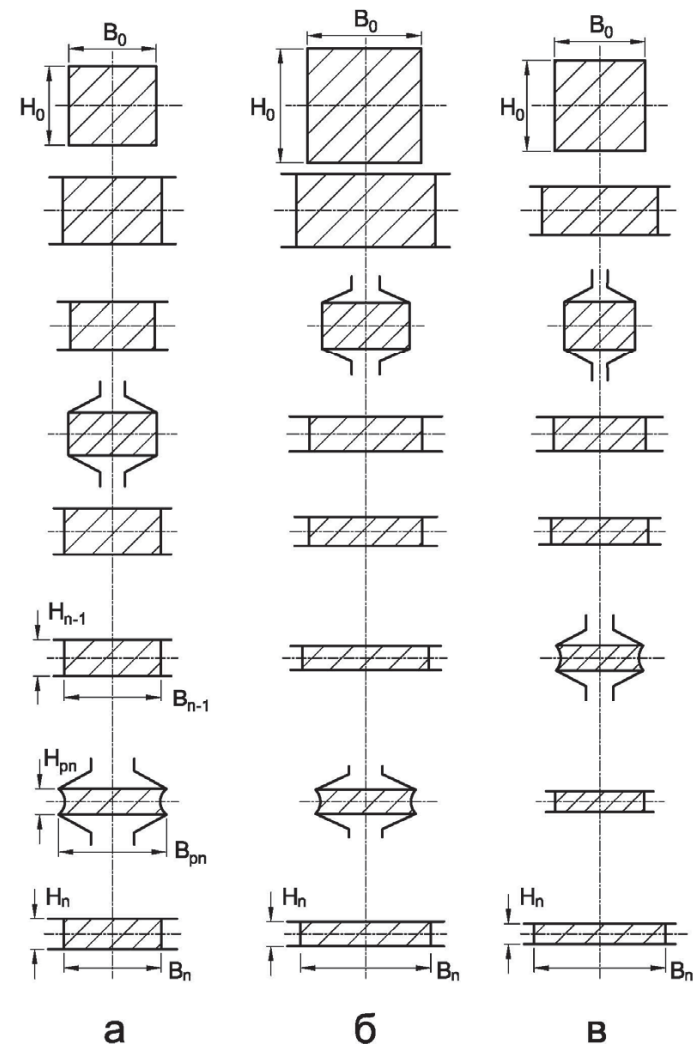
Типові схеми прокатки штабової сталі на неперервних станах
